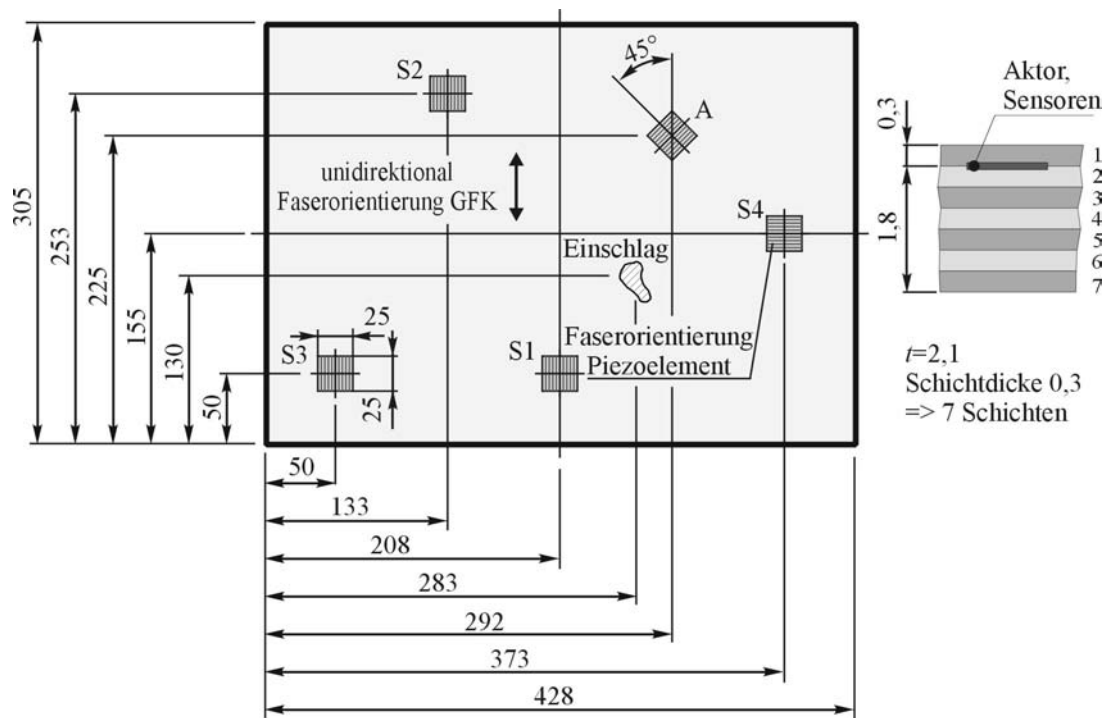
Geometrie der GFK-Platte, Schädigungsort und Positionen der Piezofasern
